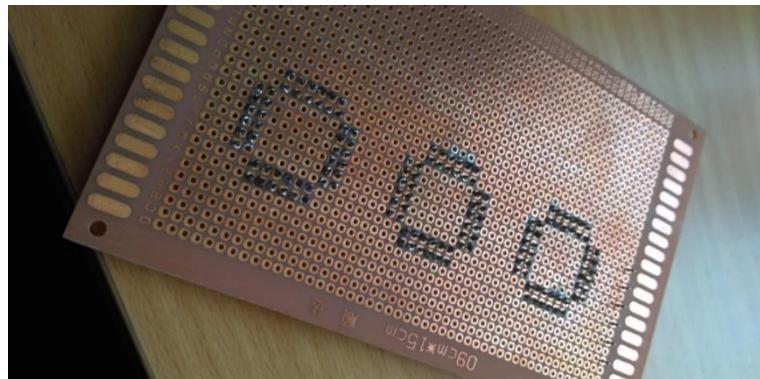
Parte trasera de la PCB con los pines de los adaptadores soldados
